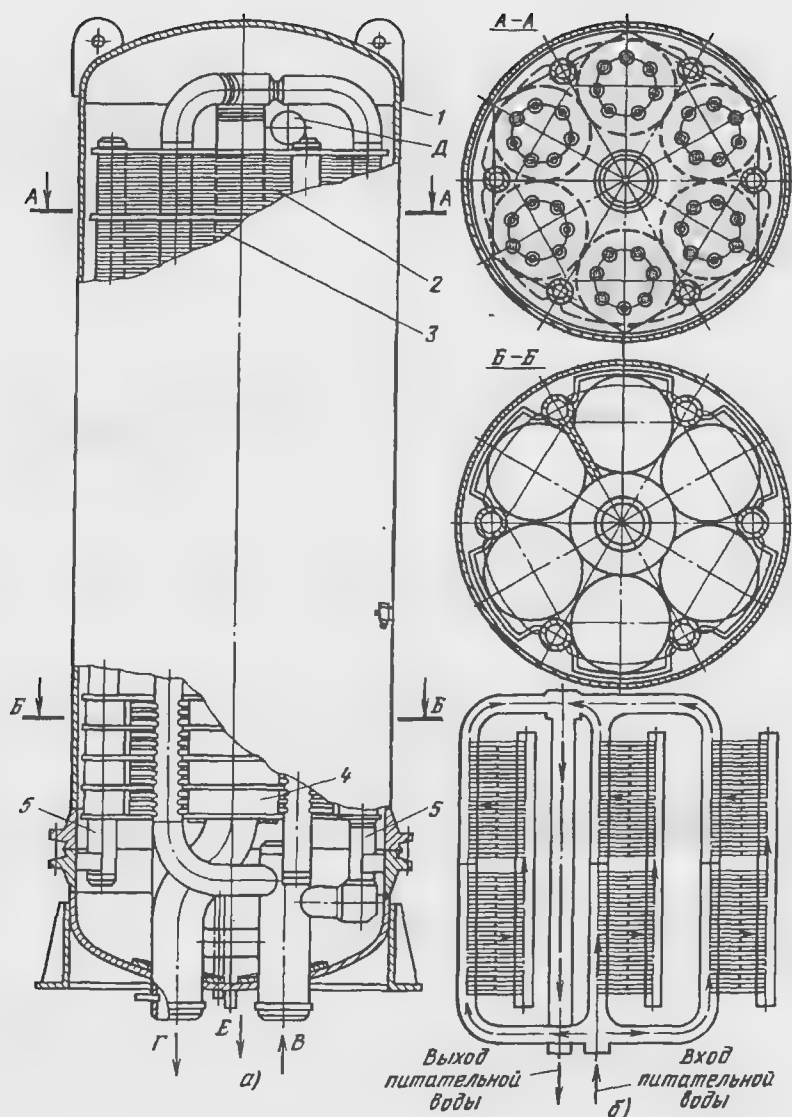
Подогреватель высокого давления ПВ-1600:
